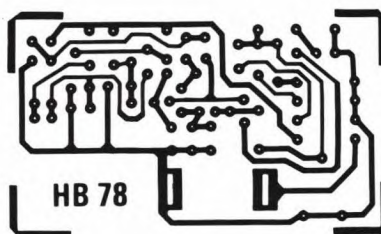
De print lay-out van de luciferadio. Vanwege het kleine printje moeten we nauwkeurig solderen!
